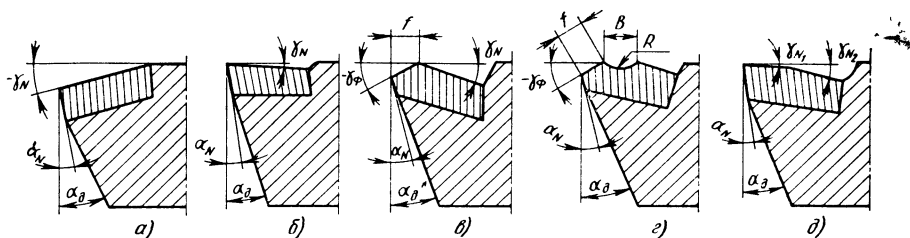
Формы заточки передней поверхности твердосплавных резцов:
